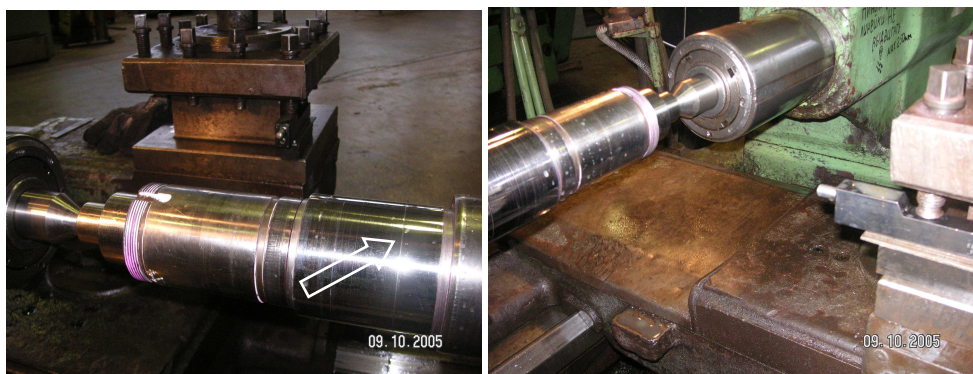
Алмазный резец Diamond в стандартном держателе токарного станка
